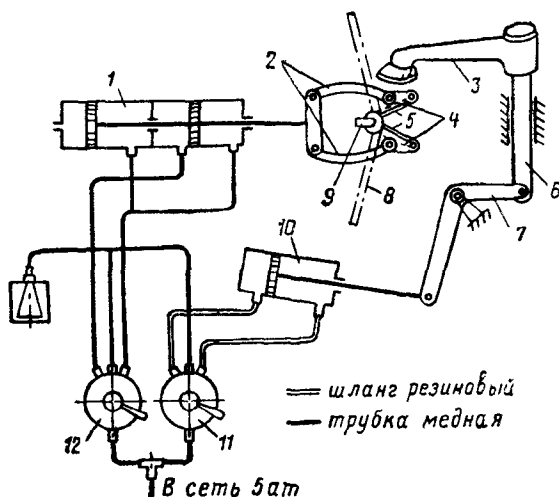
Кинематическая схема станка для изгиба головок катушек якоря
